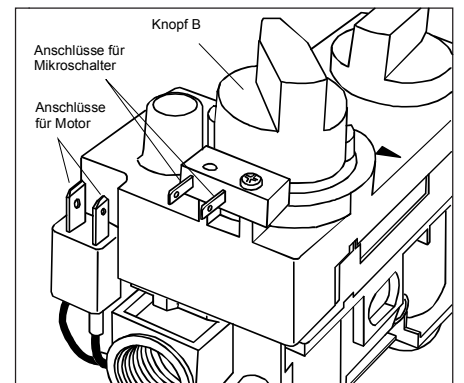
Haube mit Steckanschlüssen für Mikroschalter und Motor
